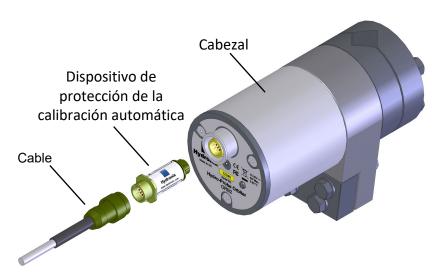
Conexión del dispositivo de protección de la calibración automática
